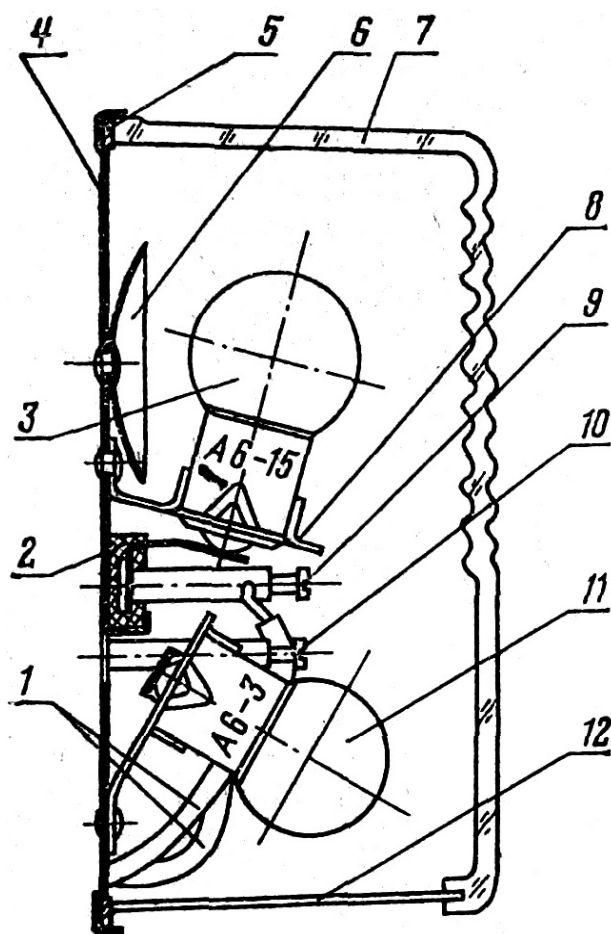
Задний фонарь ФП-246: 1 — провода; 2 — изолирующая подушка; 3 — лампа стоп-сигнала; 4 — корпус; 5 — прокладка; 6 — отражатель; 7 — рассеиватель; 8 — патрон; 9 — клемма стоп-сигнала; 10 — клемма подсветки номерного знака; 11 — лампа подсветки номерного знака; 12 — стекло подсветки номерного знака
